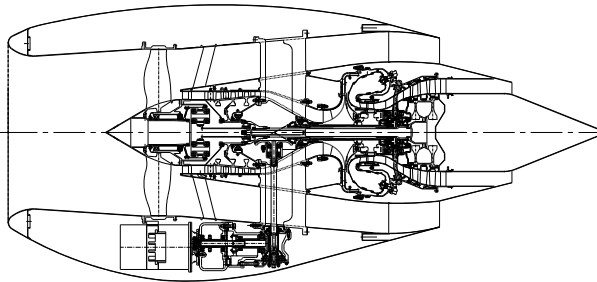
Турбореактивный двухконтурный двигатель степенью двухконтурности больше 8
